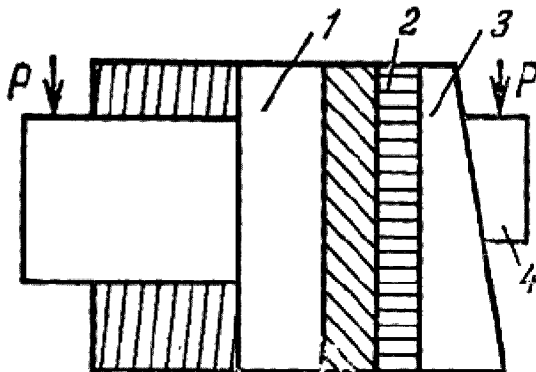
Опрессовывание изоляции втулки контактных колец: 1 — втулка; 2 — изоляция; 3 — вкладыши пресс-формы; 4 — прессовочное кольцо
